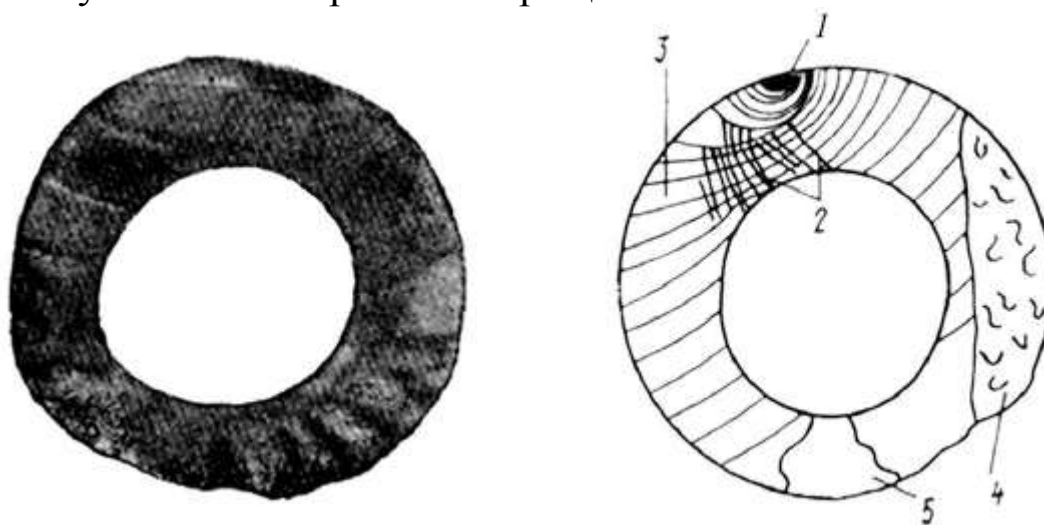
Усталостный излом (слева) и схема излома (справа) шатунной шейки коленчатого вала с типичными знаками из стали 40ХНМА
